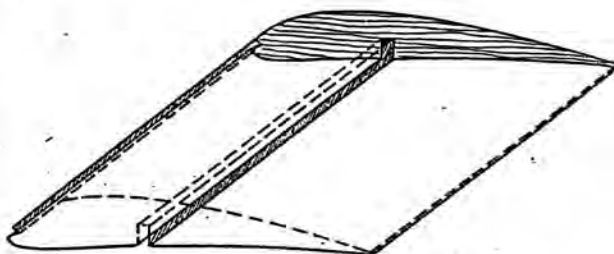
Der Holzblock mit ausgearbeitetem Profil und Nuten für die Holme
